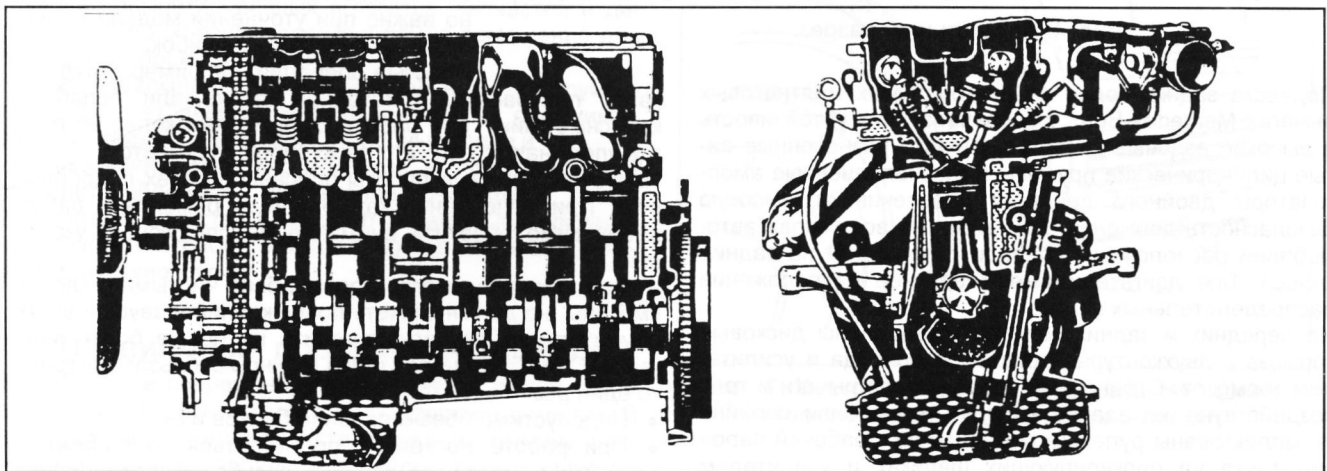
Продольный и поперечный разрезы двигателя M110 с впрыском топлива.
